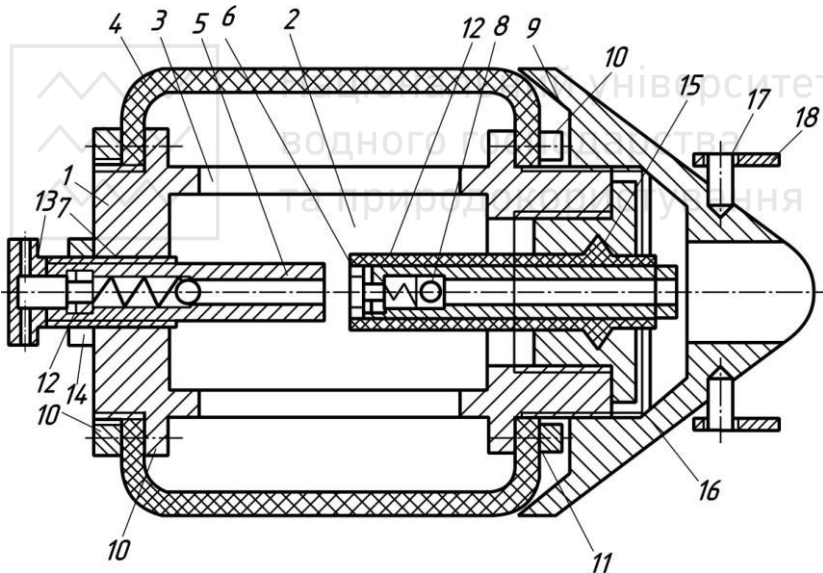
Конструкція електрогідролічного дренаера: 1 – корпус; 2 – місткість для робочої рідини; 3 – напрямні вікна; 4 – еластична оболонка; 5, 6 – електроди; 7, 8 – напірний і всмоктувальний клапани; 9 – конусний ковпак; 10 – гайки із шплінтами; 11, 12 – регулювальні гайки; 13 – гайка-перфоратор; 14 – контргайка; 15 – ізоляційний корпус; 16 – гайка; 17 – шарніри; 18 – тягова скоба
